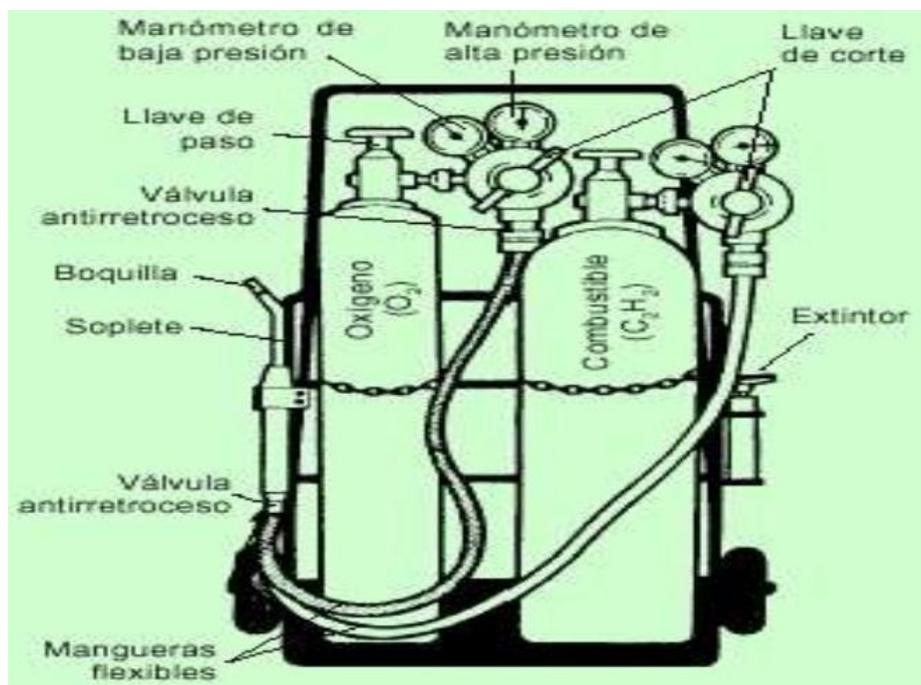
PARTES DEL EQUIPO DE SUELDA AUTÓGENA
